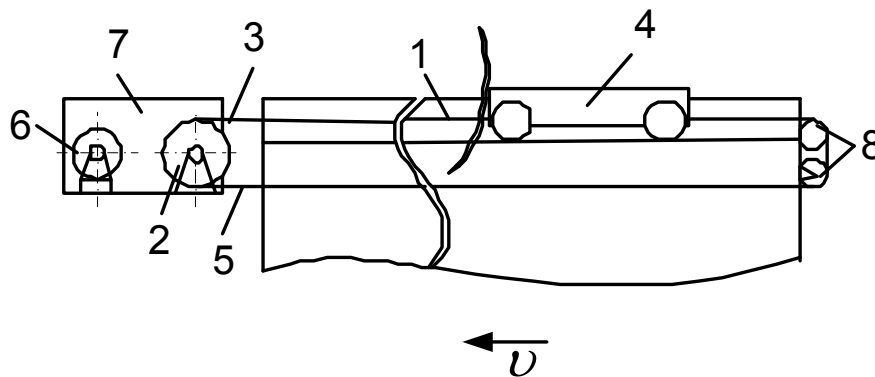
Схема запасовки канатов: 1 – канат; 2 – барабан; 3 – ветвь набегающая; 4 – тележка; 5 – ветвь сбегающая; 6 – двигатель; 7 – коробка передач автомобильная; 8 – блоки неподвижные; v – направление рабочего движения
